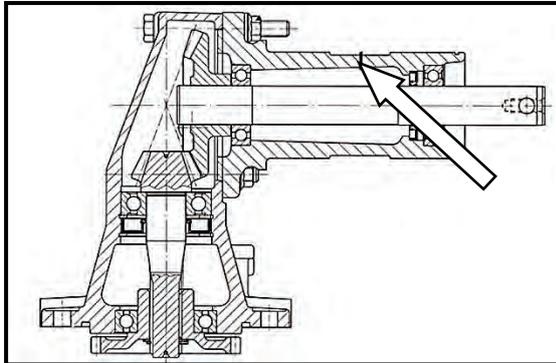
Taladro de purga en el cuello del cojinete del engranaje angular
